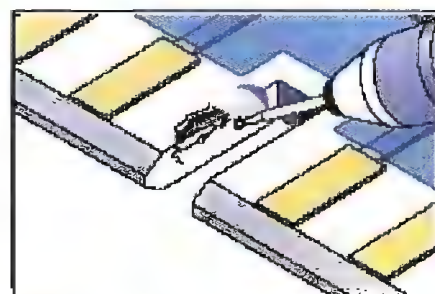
Фрезеровать поврежденный материал подложки платы
